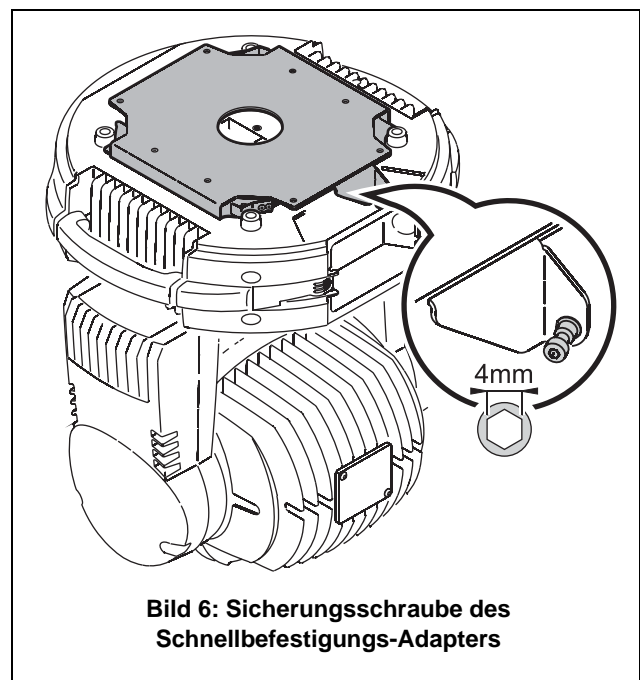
Sicherungsschraube des Schnellbefestigungs-Adapters
